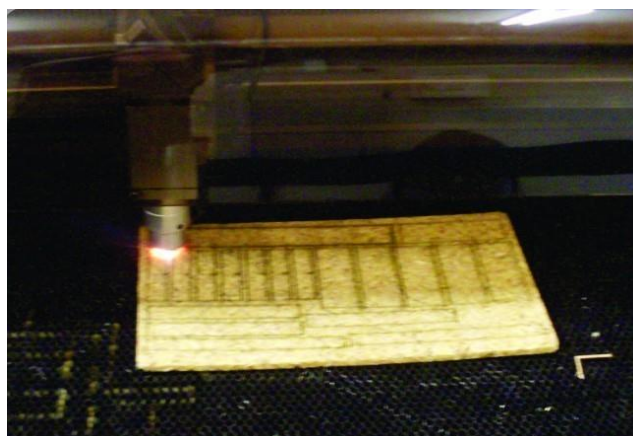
Plano de corte dos corpos de prova: A) Tração, B) Flexão, C) Absorção de água, D) Impacto.
